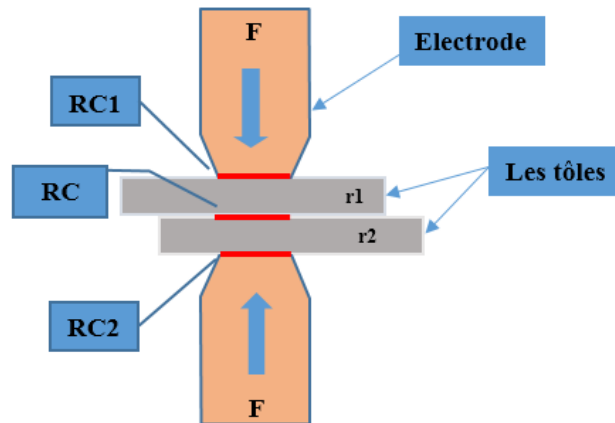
Mécanisme de formation de point de soudure par résistance par point [9]
